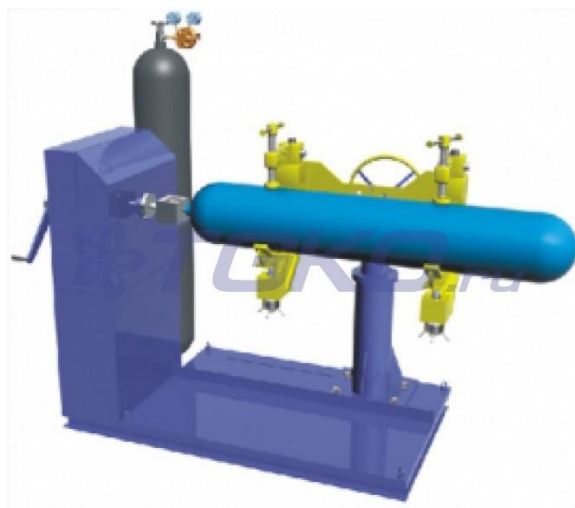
Стенд для демонтажа вентиля с баллона ДВк
